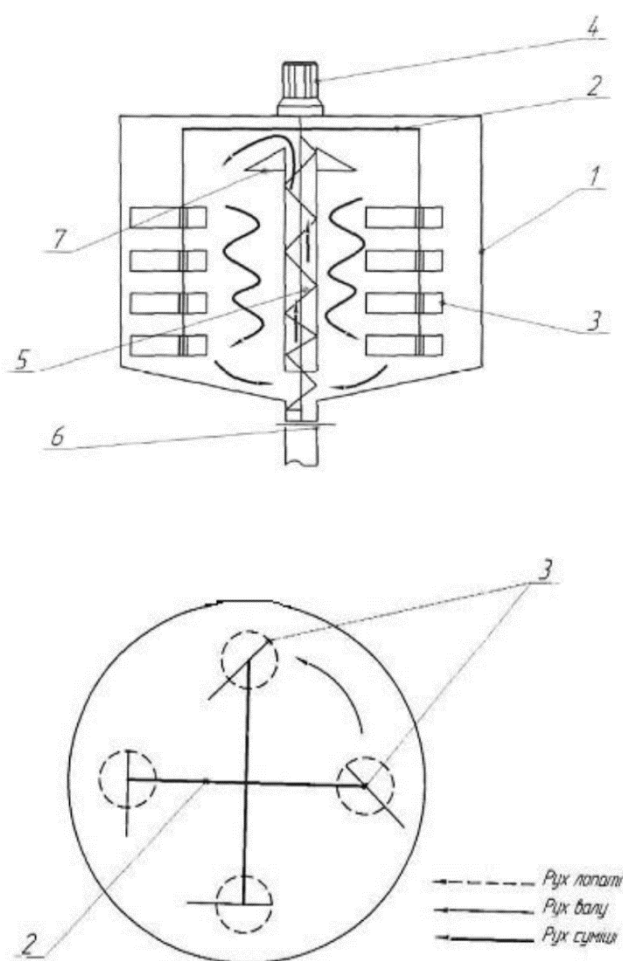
Змішувач за патентом № 60687: 1 – корпус-ємність; 2 – вал мішалок; 3 – несиметричні лопаті; 4 – електродвигун; 5 – вал шнека; 6 – вікна вивантаження; 7 – лоток.
